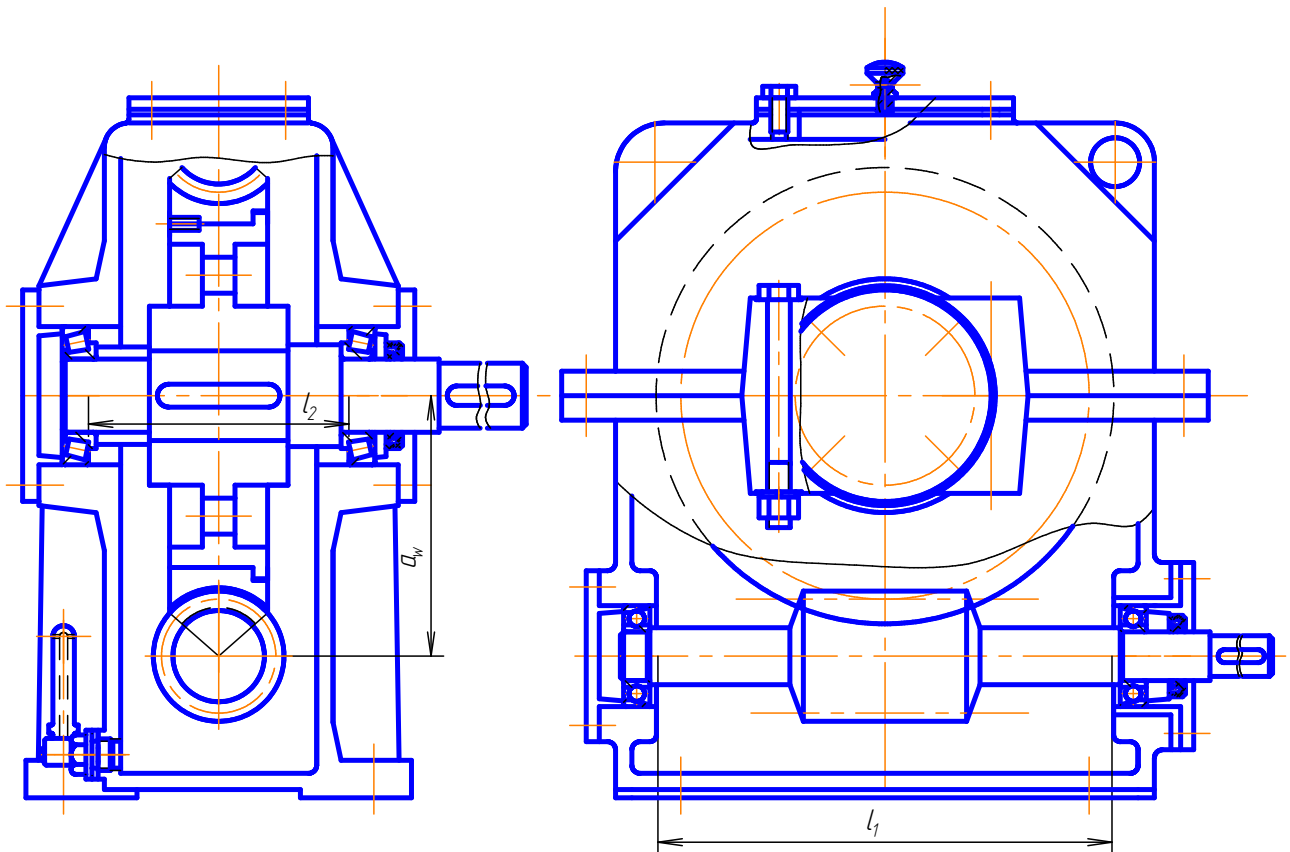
Пример конструктивной компоновки червячного редуктора
